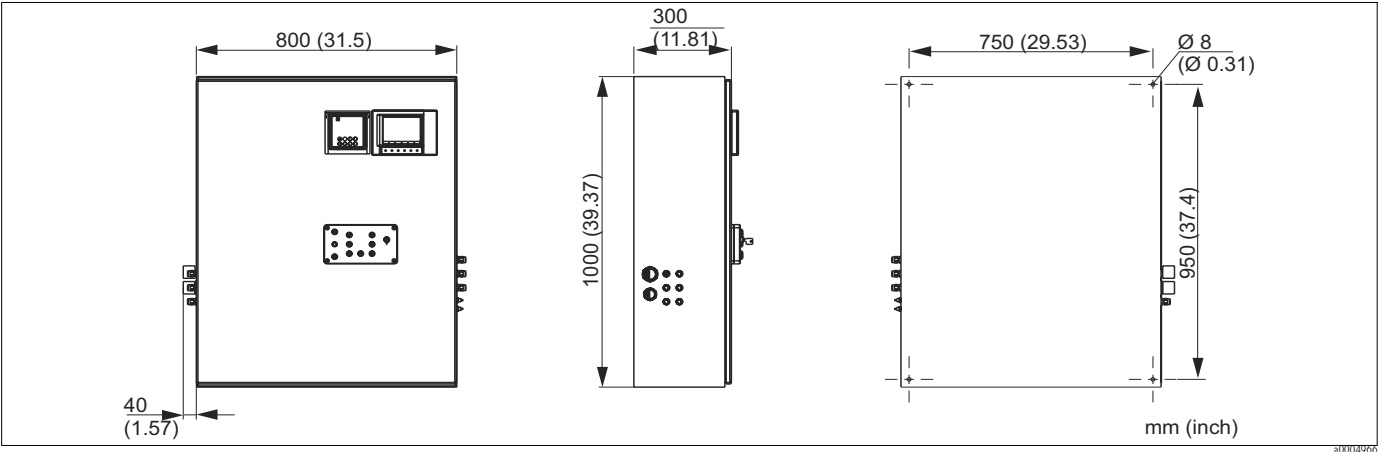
Dimensions du boîtier CYC310, version matière synthétique
